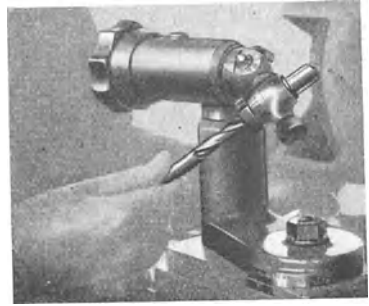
Spiralbohrer-Spitzenschleifmaschine für kleine Bohrer. (R. Stock & Co., Berlin.)
